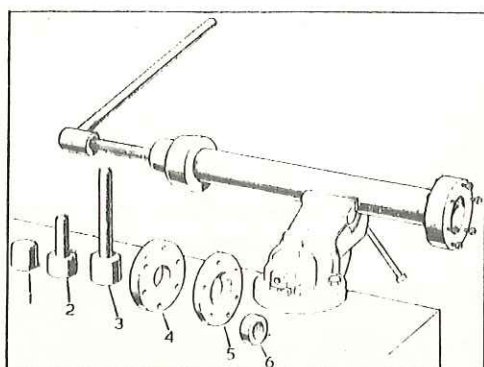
Util para el desmontaje y juego de adaptadores, 245178
